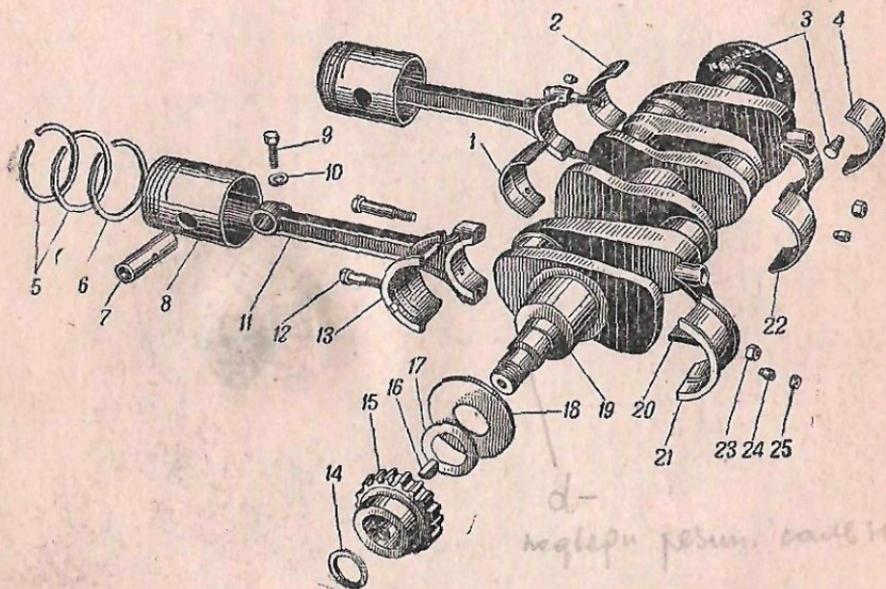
Коленчатый вал и шатуно-поршневая группа:
